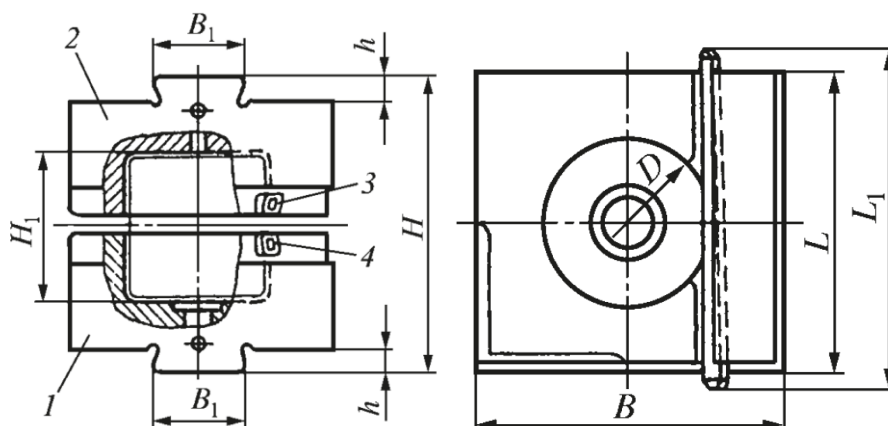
Блоки универсальные молотовых штампов с цилиндрическими вставками [2]: 1 — нижний блок; 2 — верхний блок; 3 — верхний клин; 4 — нижний клин
